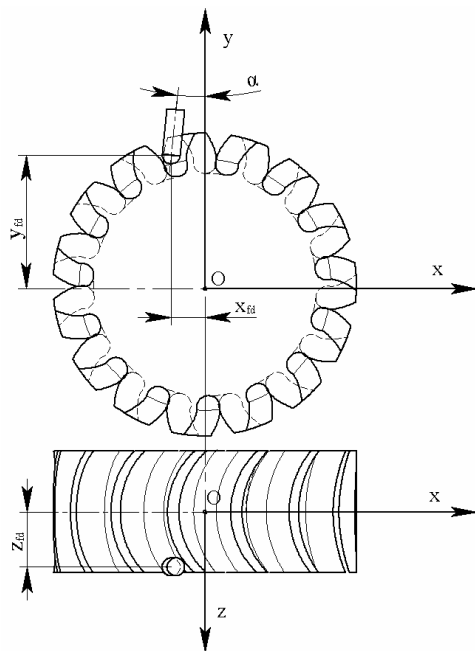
Текущее положение пальцевой фрезы при нарезании арочного зуба на 5-ти координатном станке
